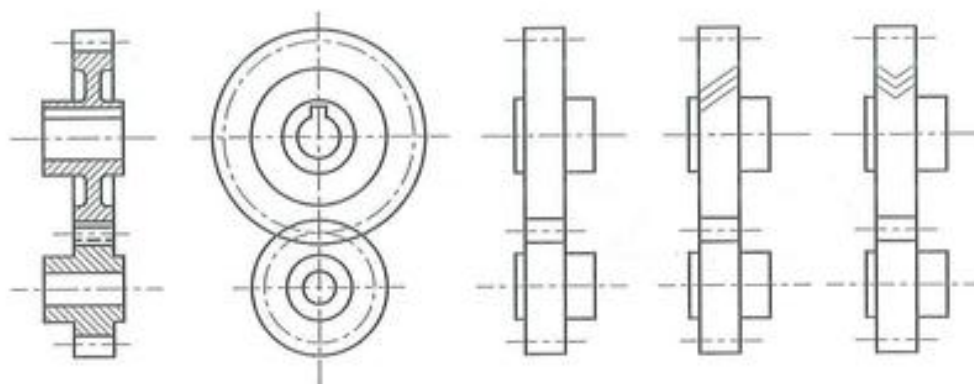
Engranajes exteriores de ruedas cilíndricas.
